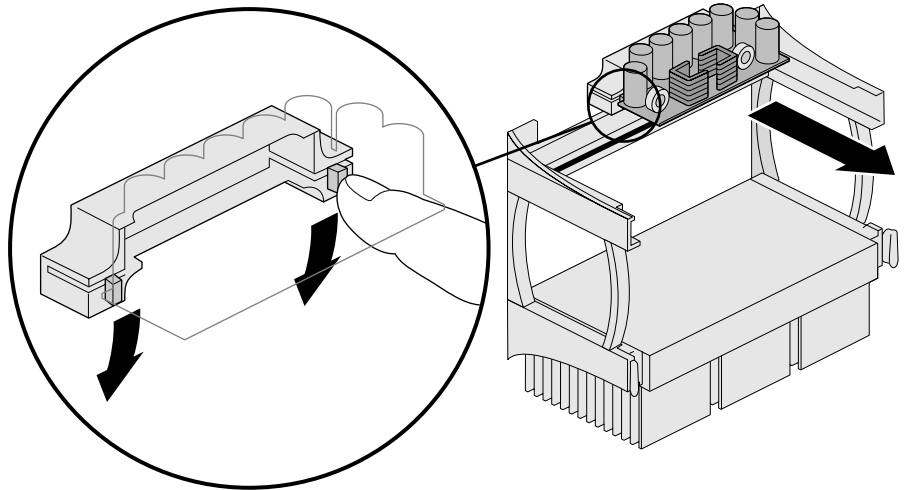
Desconexión del cable de la fuente de alimentación del ventilador del procesador de la tarjeta
